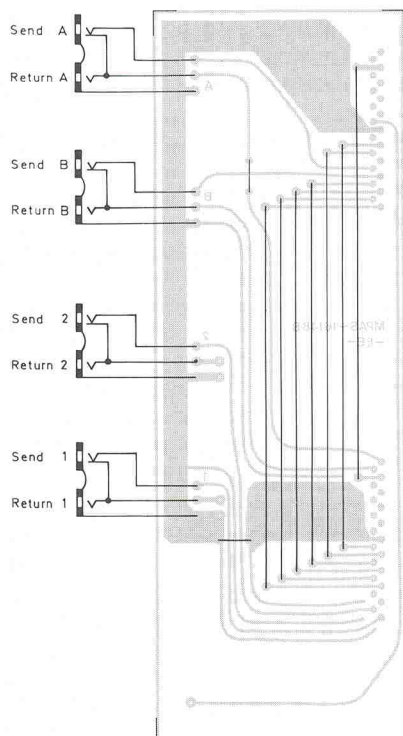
Die ECB-Platine wird nur mit einigen Drahtbrücken bestückt.
